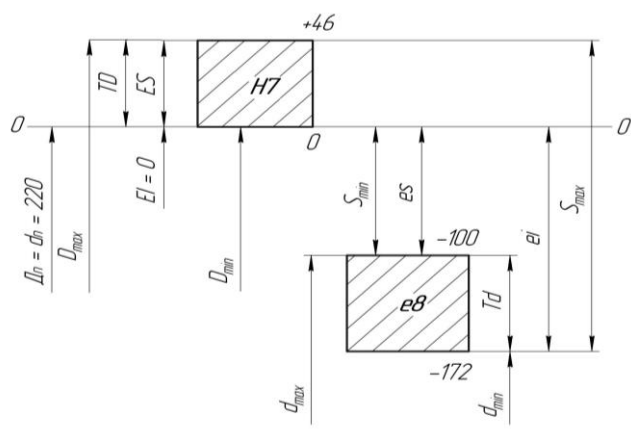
Схема полей допусков для посадки с зазором (пример)
